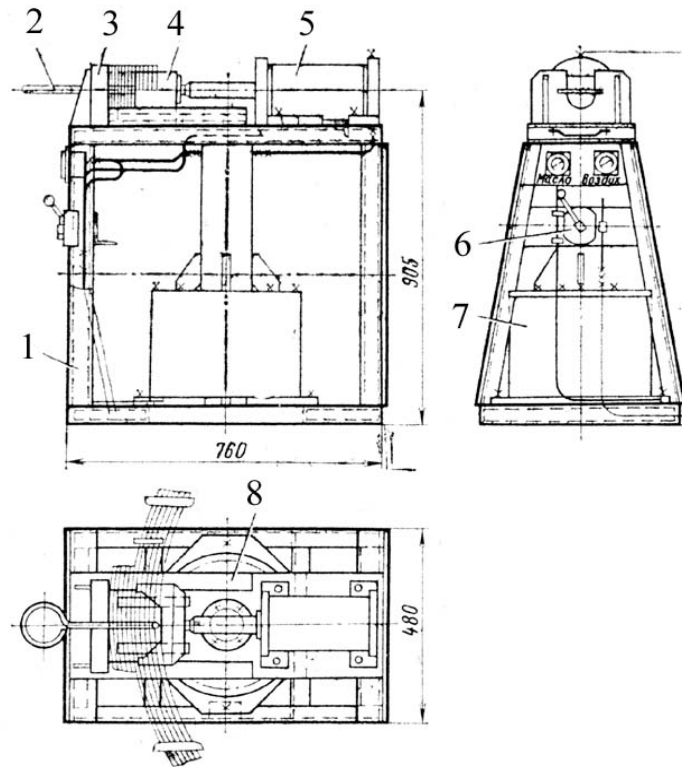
Стенд моделі 3039: 1 – основа; 2 – штир; 3 – упор; 4 – повзун; 5 – гідроциліндр; 6 – рукоятка крана; 7 – пневмоциліндр; 8 – напрямні.
